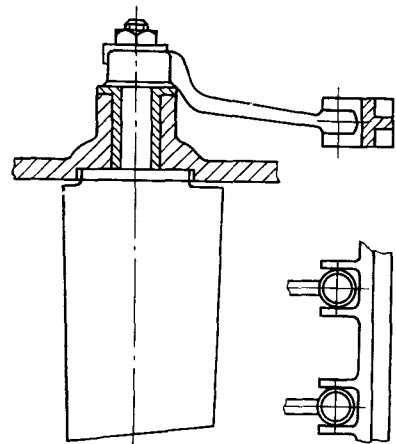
Поворотный направляющий аппарат компрессора авиационной ГТУ
